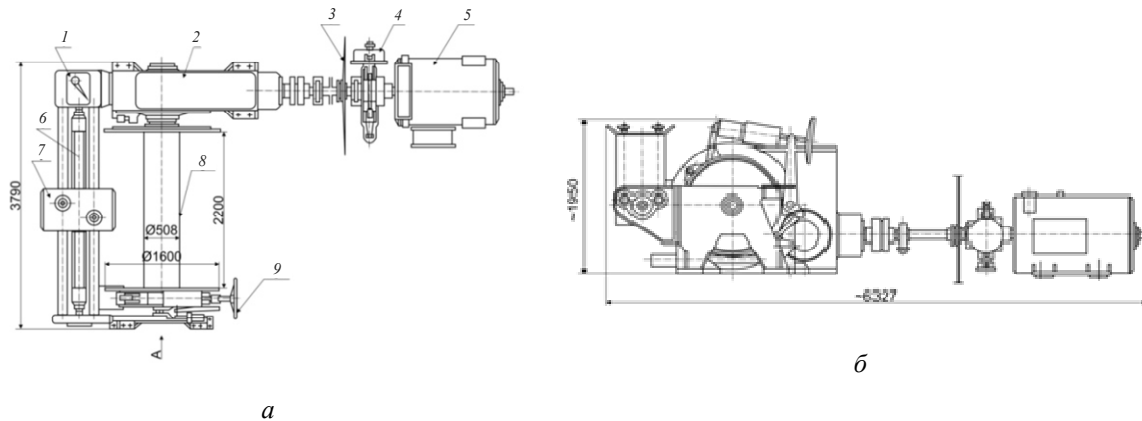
Ваерная лебедка ПНР WTJ12,5 W290Z1: а – вид сверху:
